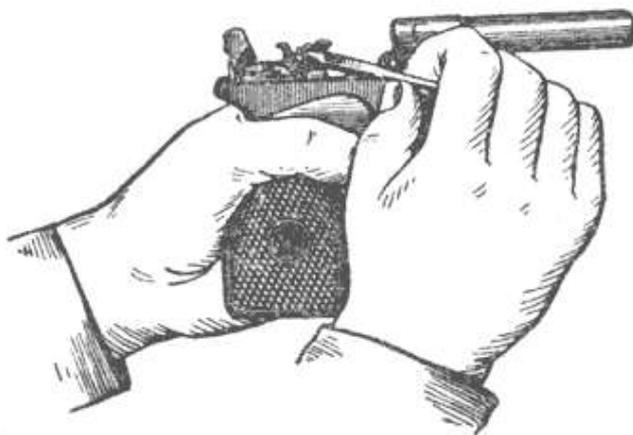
Снятие крючка пружины шептала с затворной задержки
